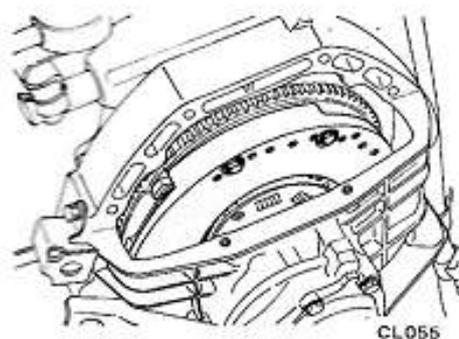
Dépose des vis de fixation du couvercle d'embrayage
